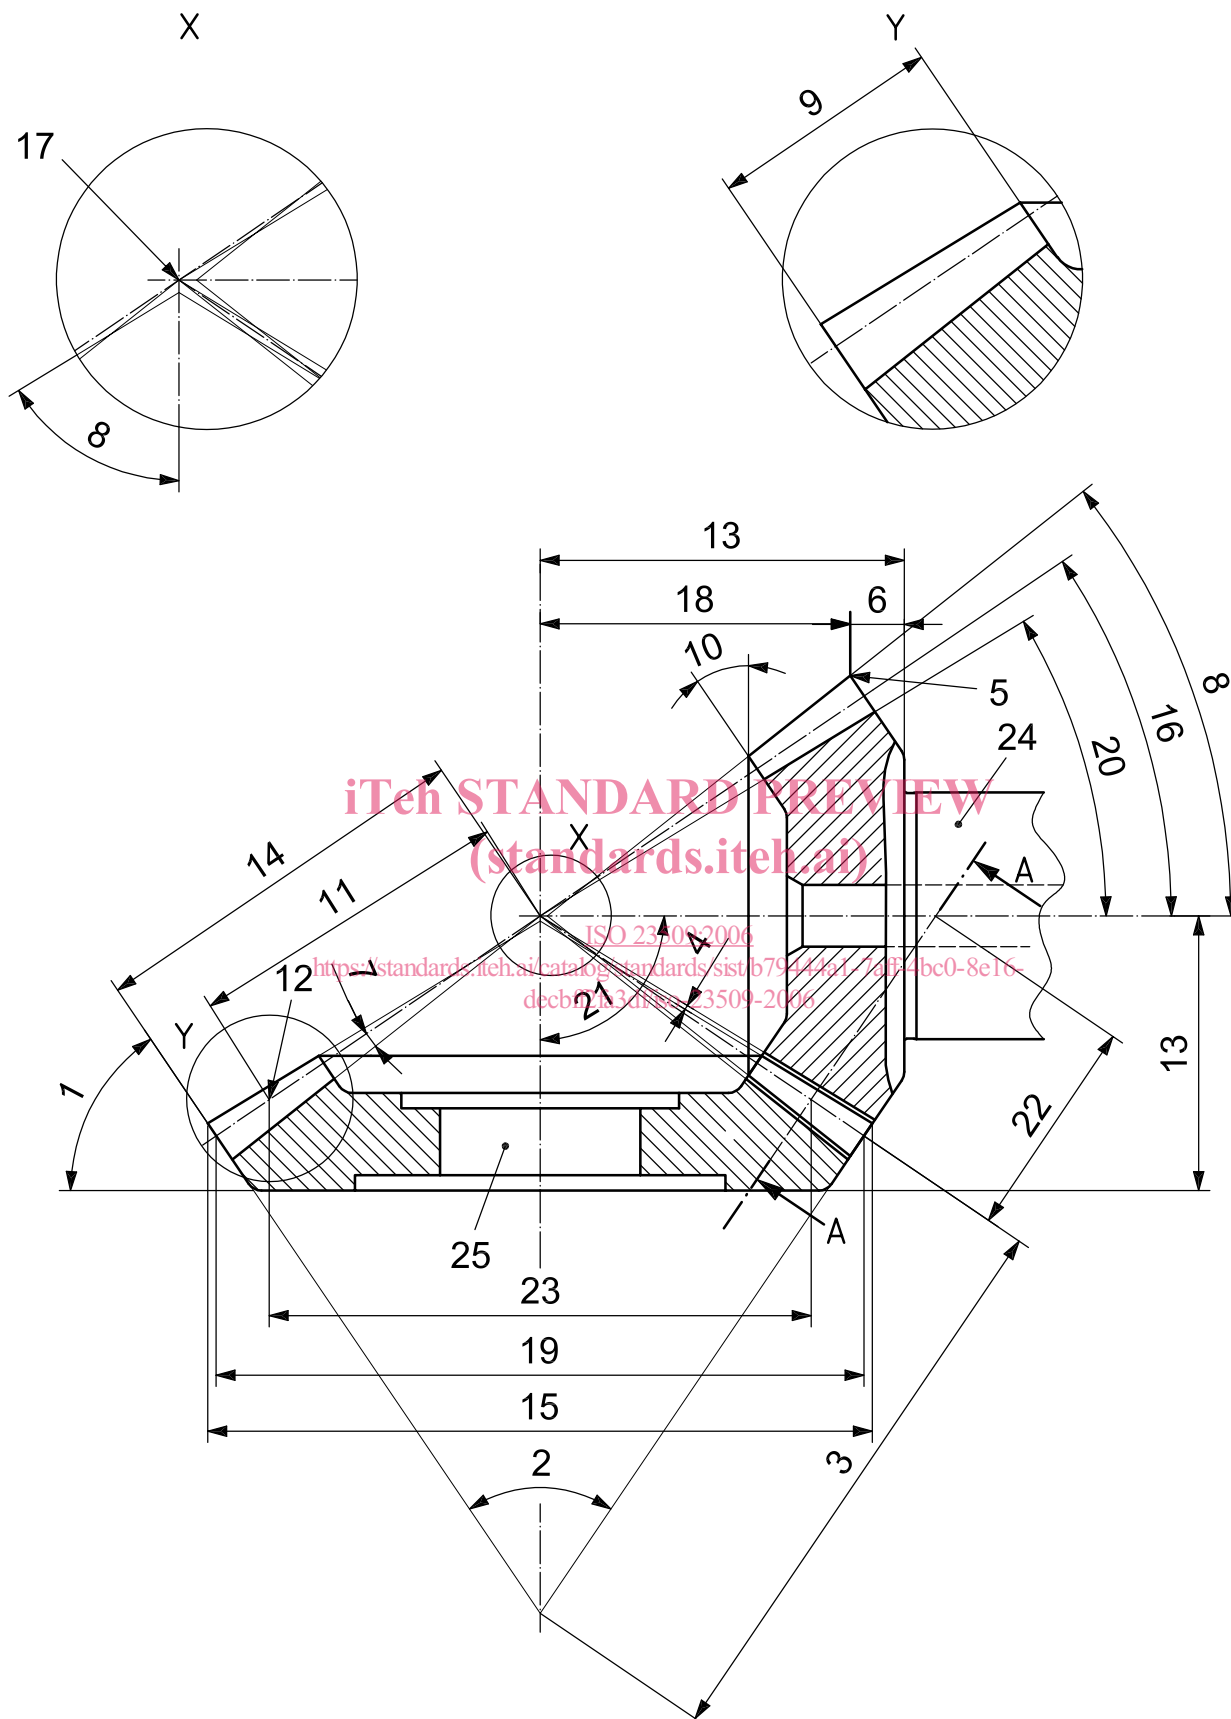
Nomenclature d'un engrenage conique — Plan axial
